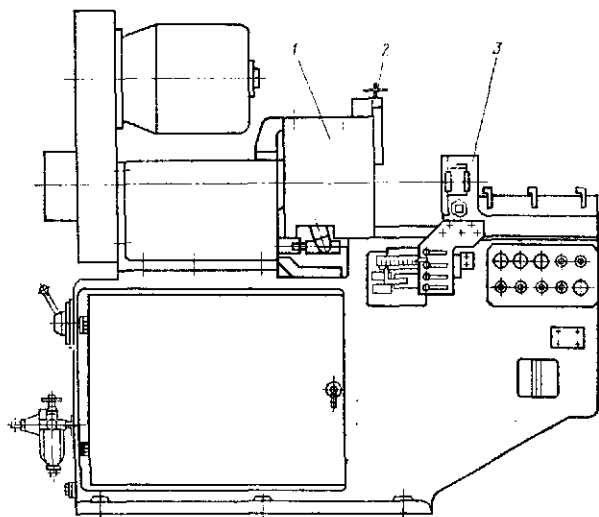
Механизм для накатки резьбы на трубах СТД-129
